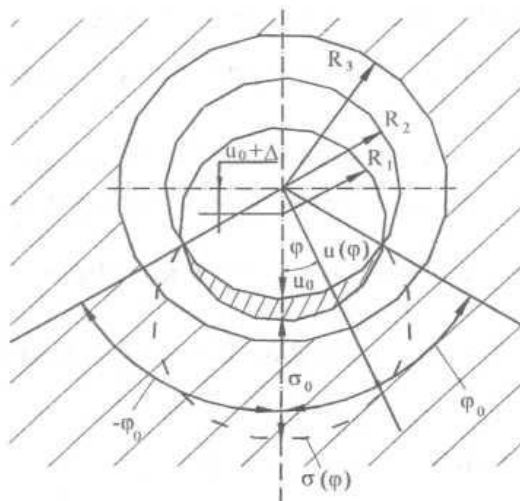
Розрахункова схема підшипника ковзання
